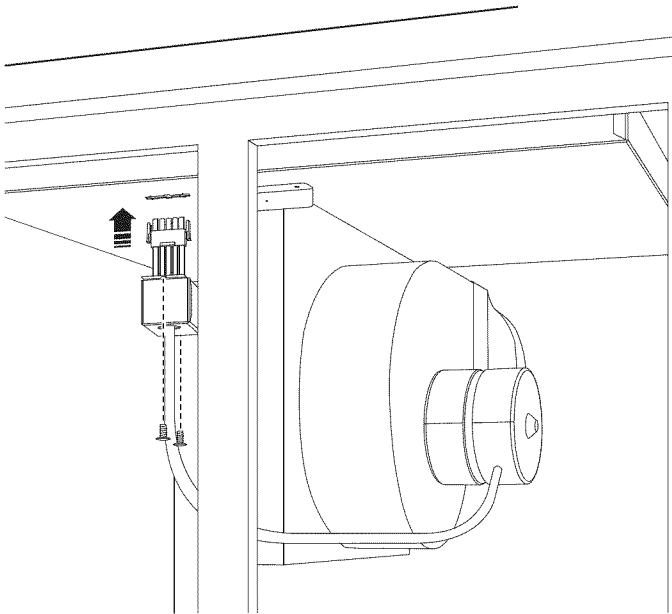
CONEXIÓN DEL VENTILADOR A LA PLANCHA
